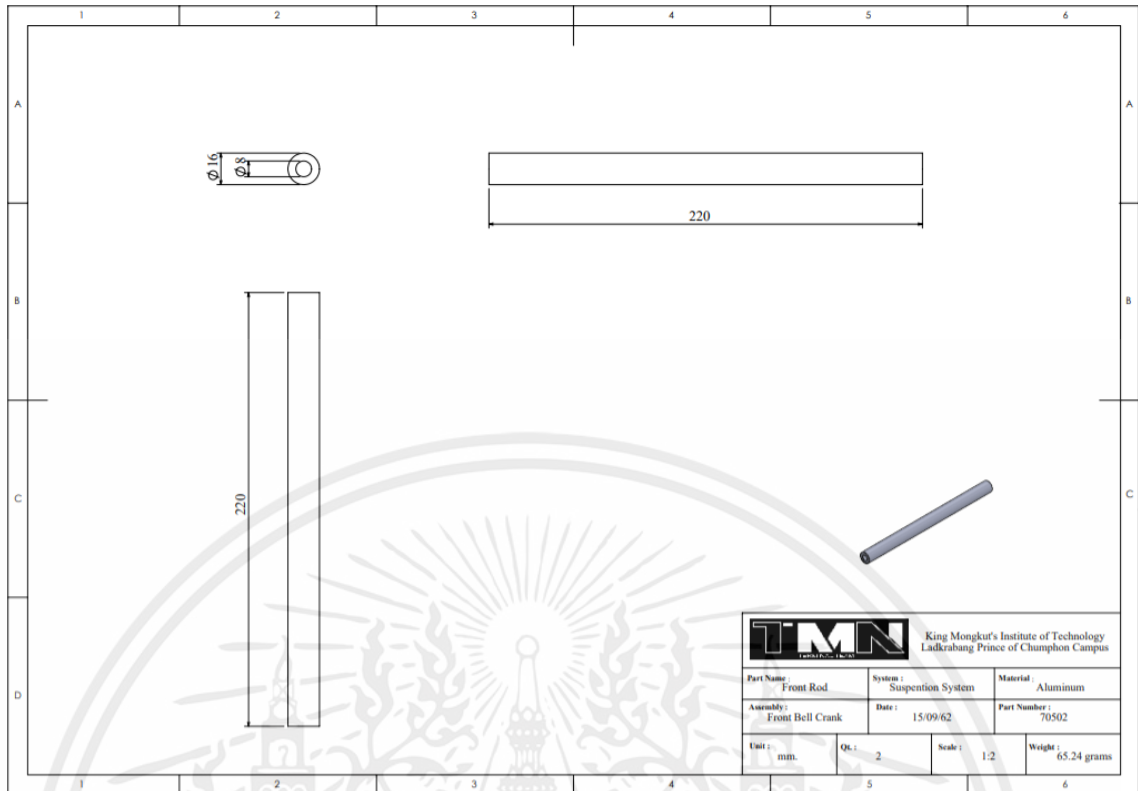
ส่วนประกอบชุดกระเดื่องมุมฉาก (Front Bell Crank Assembly)
